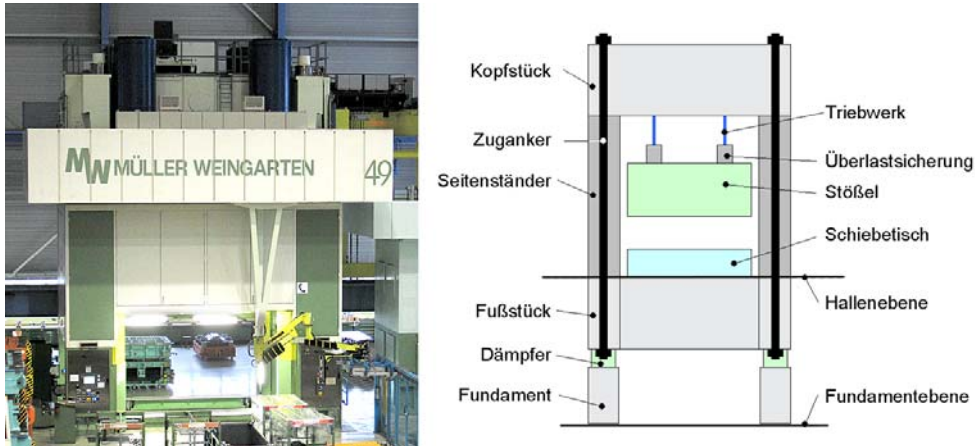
(links) Verwendete Umformmaschine; (rechts) Prinzipieller Maschinenaufbau
